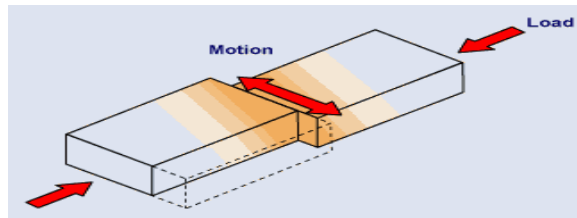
Proses *Stir Friction Welding
